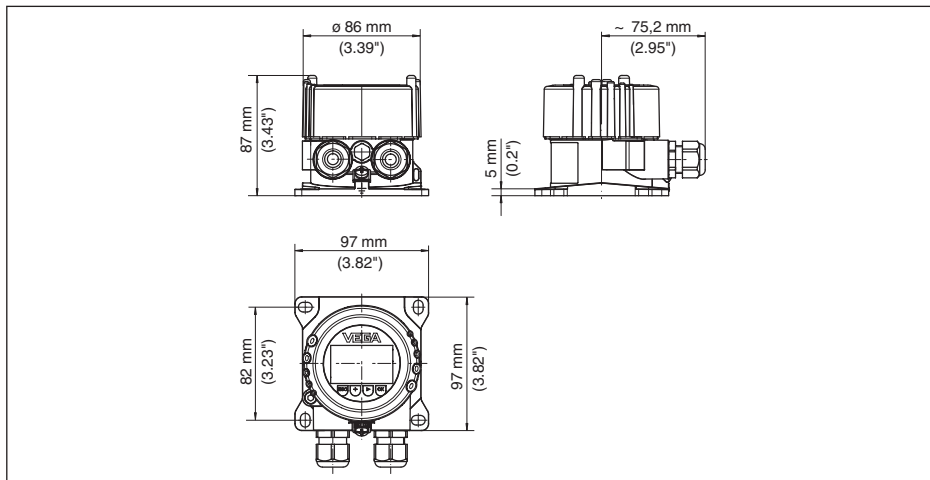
VEGADIS 82 с алюминиевым корпусом
